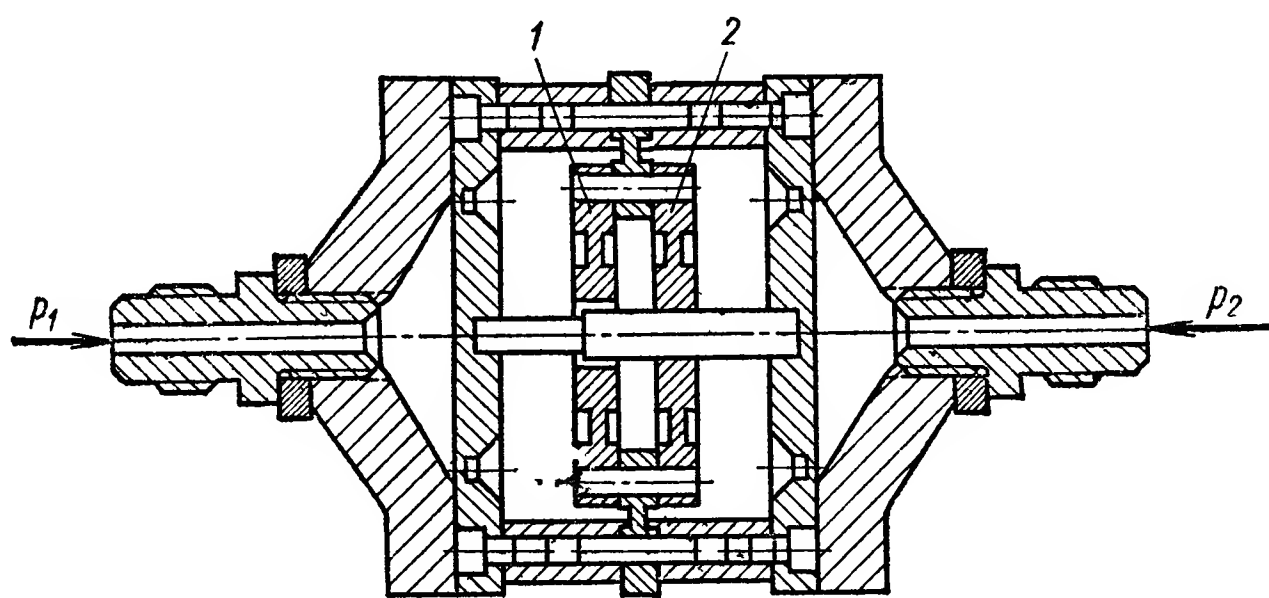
Общий вид магнитоупругого преобразователя давления
